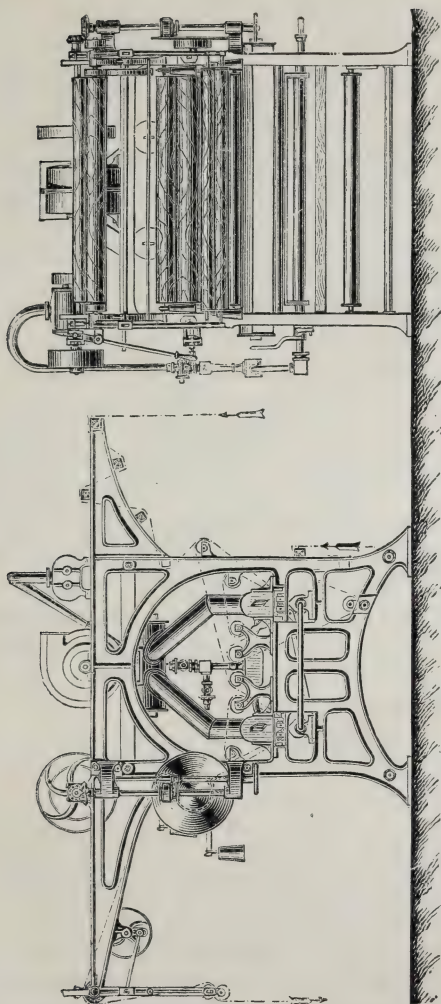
Gasfengmaschine der Zittauer Maschinenfabrik.
